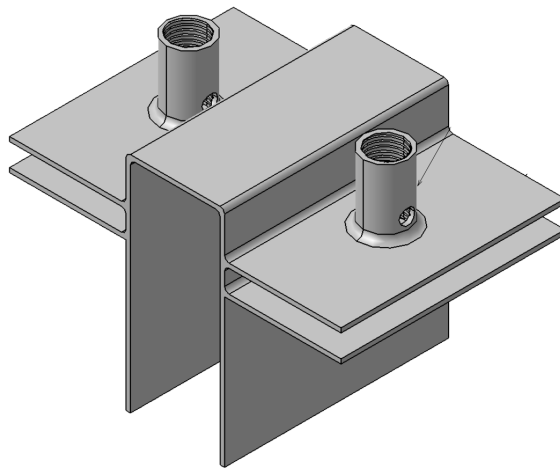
Instructivo de Uso del soporte 1 Vía utilizado para el panel
